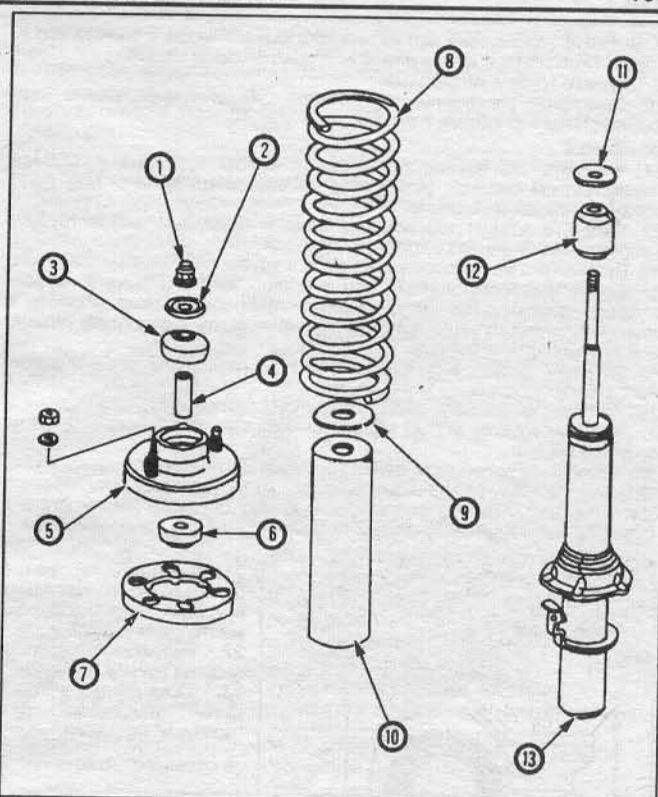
б Сборка амортизатор - пружина (модели с 1988 года): 1 - гайка крепления амортизатора; 2 - шайба; 3 - резиновая подушка; 4 - проставка; 5 - седло пружины; 6 - резиновая подушка; 7 - изолятор пружины; 8 - пружина; 9 - пыльник; 10 - кожух; 11 - шайба ограничителя; 12 - ограничитель; 13 - амортизатор.
